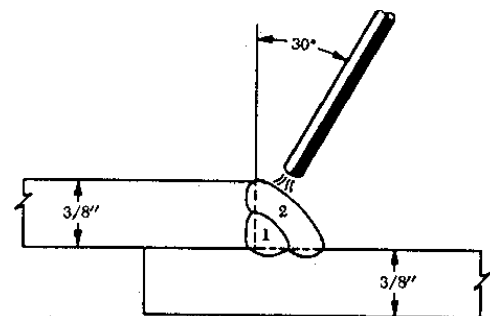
Típica justaposição dos filetes da solda de uma junta.
